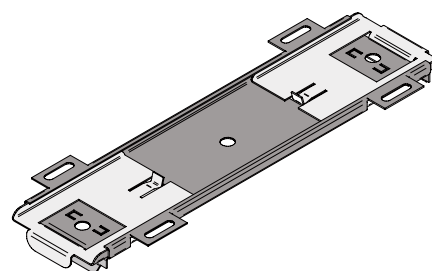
Élément d'assemblage ADRIATIC d-T-MD-4S, pour installation contre le plafond.
